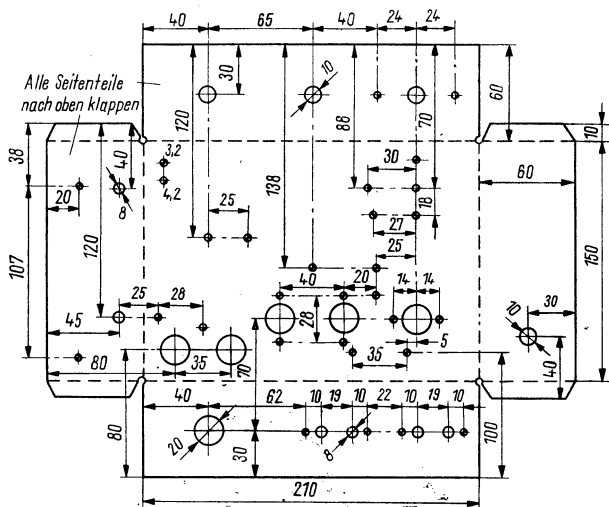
Bohrplan für das Chassis des in Bild 16 gezeigten Einkreisempfängers
